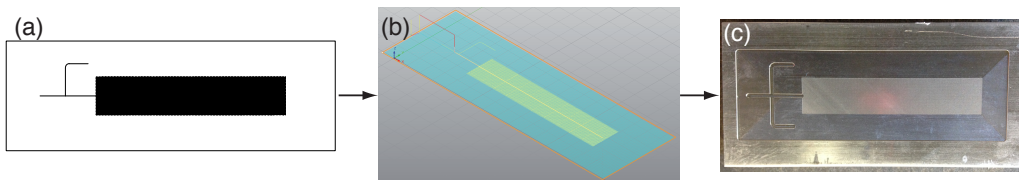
(a) Design du dispositif microfluidique à l'aide d'AutoCad. Un milieu poreux de  $50 \text{ mm} \times 10 \text{ mm}$  est relié à des canaux d'injections. (b) Trajet de la fraise généré par VisualMill à partir du design précédent. (c) Moule en aluminium réalisé avec la microfraiseuse. Le milieu poreux fait  $50 \text{ mm} \times 10 \text{ mm}$  tandis que les canaux d'injections font  $1 \text{ mm}$  de large.
